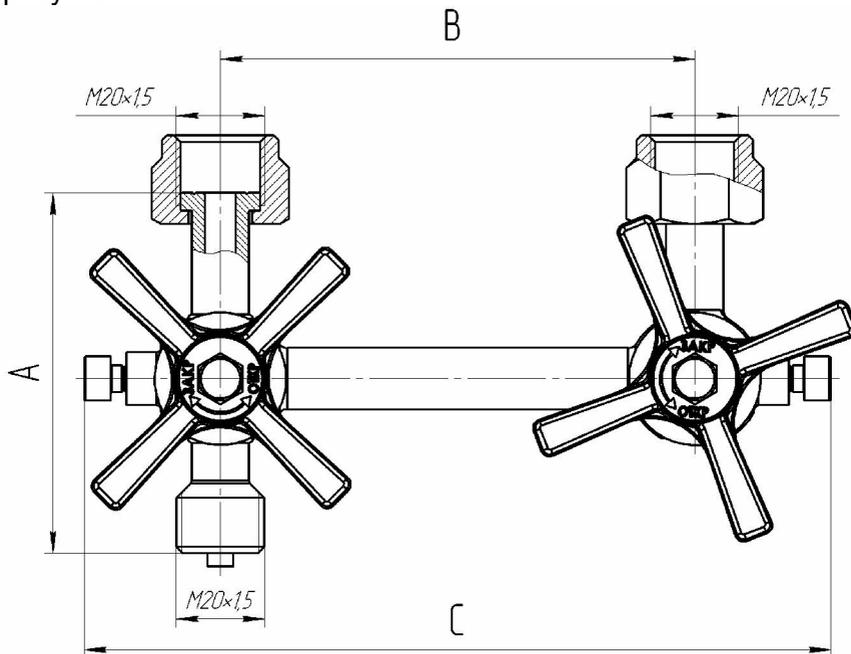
Габаритные и присоединительные размеры изделий 2xВИГ
